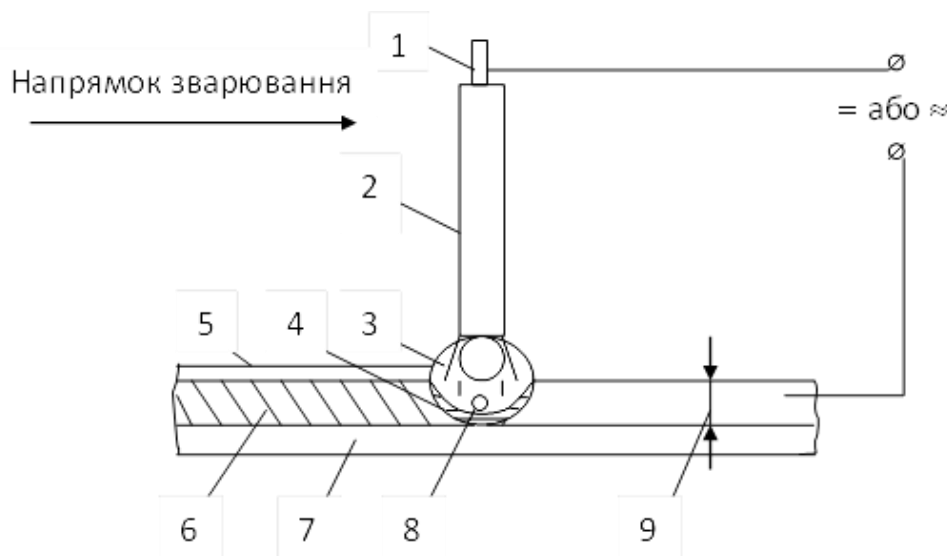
Схема процесу ручного дугового зварювання покритими електродами: 1 – металевий стержень; 2 – покриття електроду; 3 – газова атмосфера зварювальної дуги; 4 – зварювальна ванна; 5 – затверділий шлак(шлакова кірка); 6 – закристалізований метал шва; 7 – основний метал; 8 – краплі розплавленого електродного металу; 9 – глибина проплавлення.
